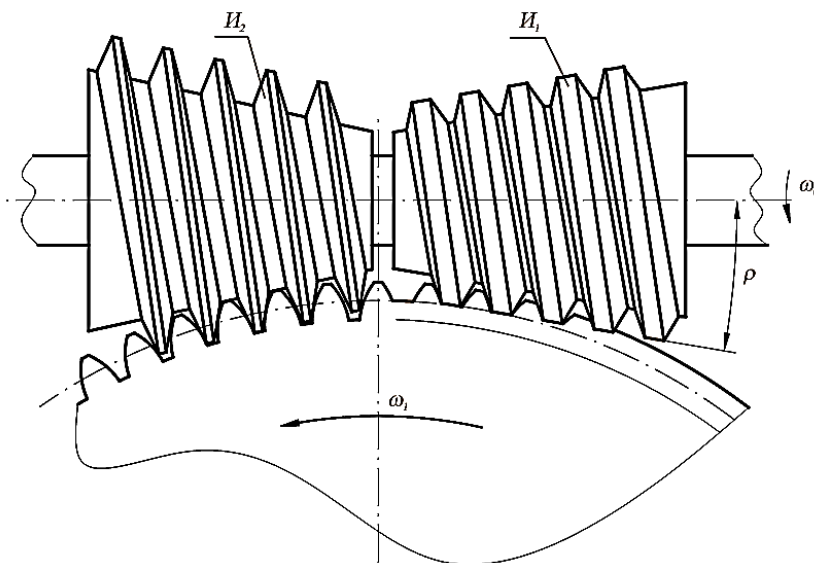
Схема формообразования двумя коническими червячными фрезами цилиндрических зубчатых колес
